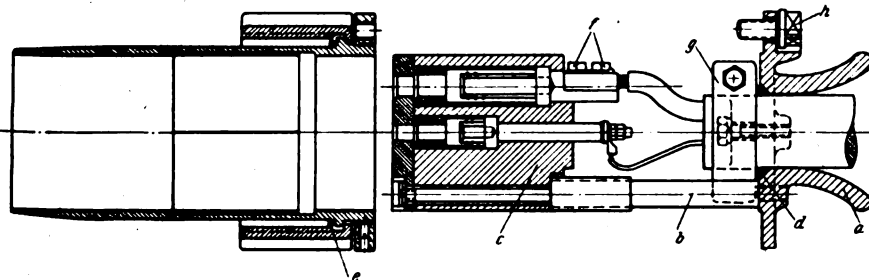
Stecker für schlagwettergeschützte elektrische Schrämmaschine.
